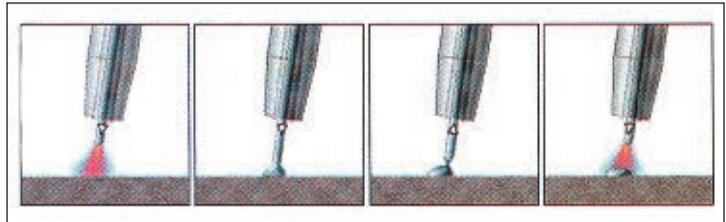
Горение дуги, направление перемещения проволоки и переход металла при СМТ сварке
